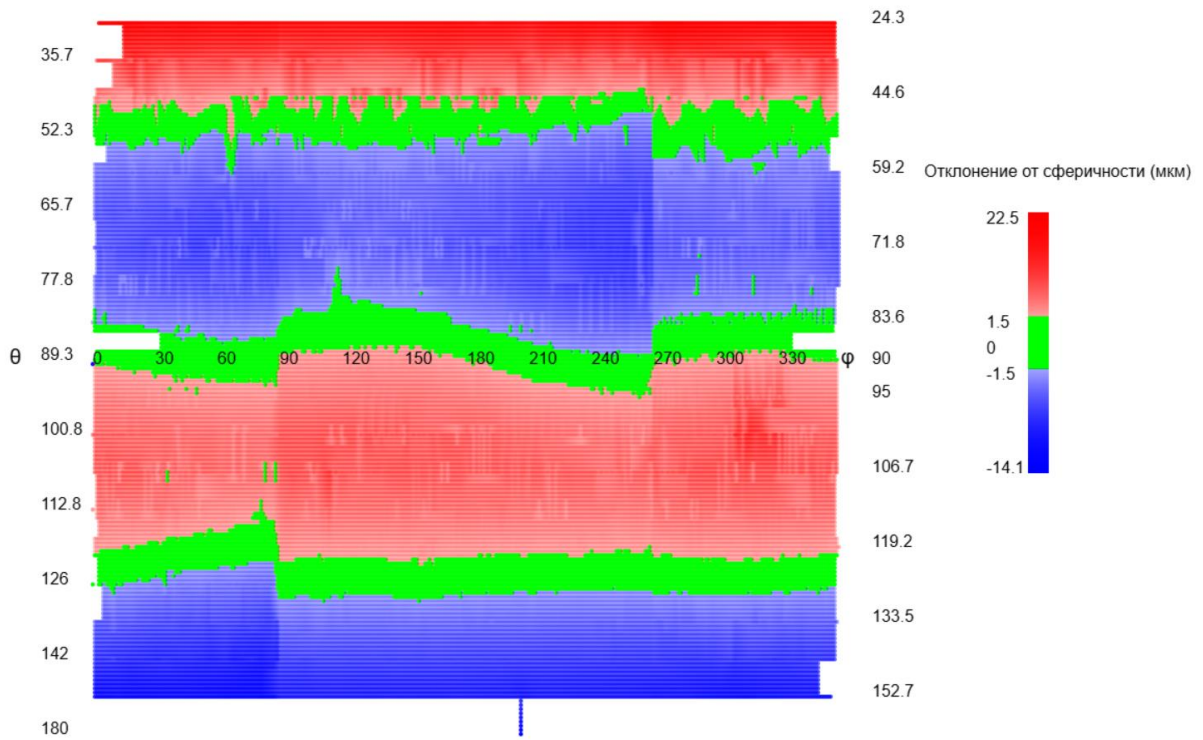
Развертка сферической поверхности шарового пальца №4 до притирки
